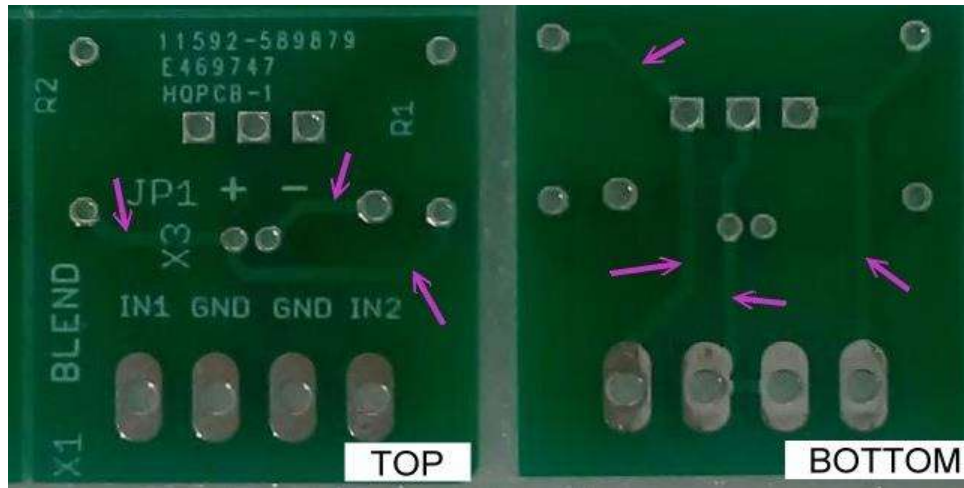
capas TOP y BOTTOM en una PCB de 2 capas de cobre [58]
